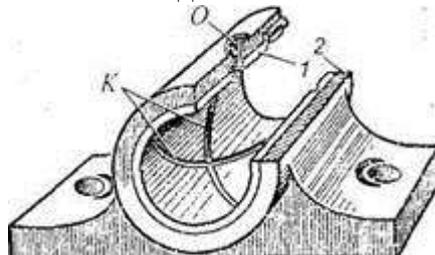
Неразъемный подшипник скольжения: 1 — втулка; 2 — корпус
